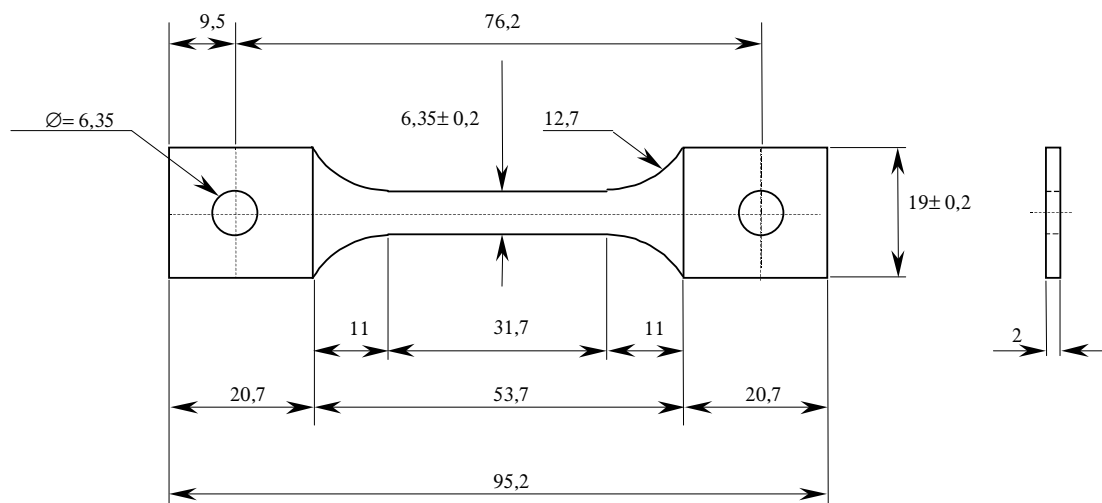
Dimensões do corpo-de-prova de tração para chapas conforme norma ASTM A370. Dimensões em mm.
